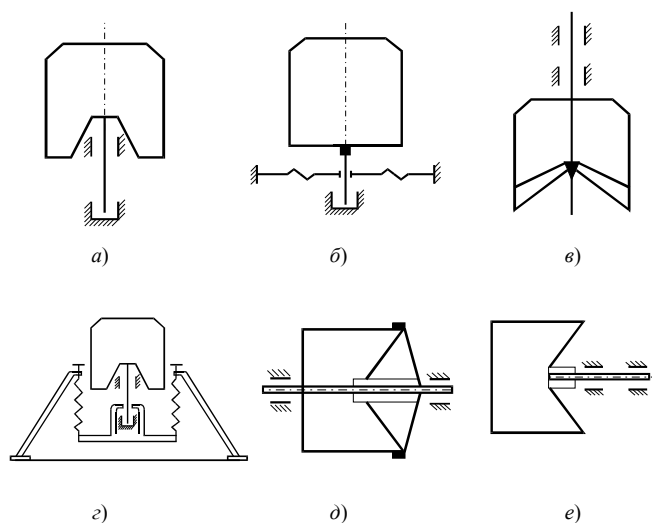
Схемы расположения ротора и крепления валов роторов:
